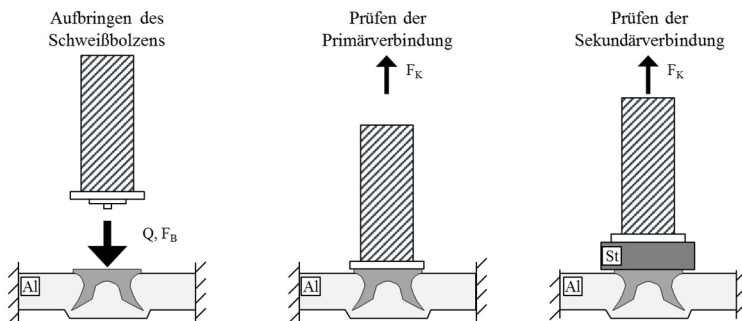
Schematischer Ablauf der Bolzenschweißung (links), Kopfzugprüfung (mitte, rechts)
